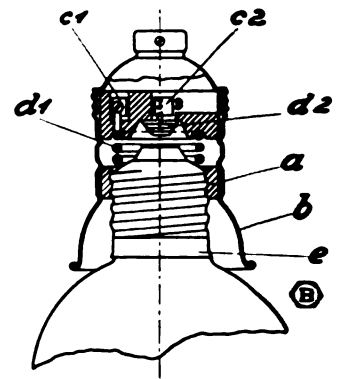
Berührungsschutzfassung mit federndem Außenkontakt.
